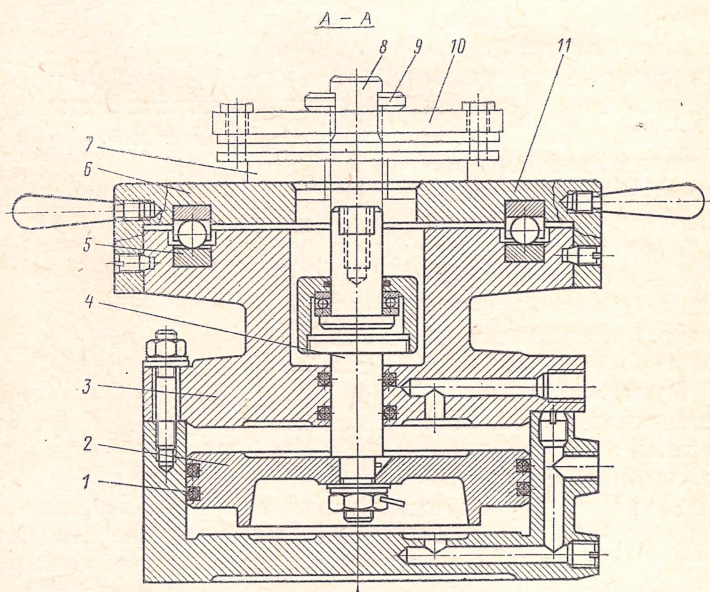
Групповое приспособление к вертикально-сверлильному станку
